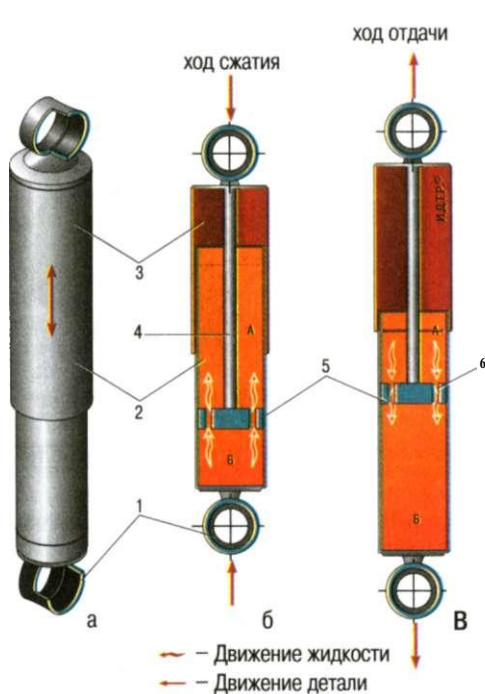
Схема работы амортизатора: а - внешний вид; б и в - принцип работы; 1 - проушина; 2 - рабочий цилиндр; 3 - кожух; 4 - шток; 5 - поршень; 6 - калиброванное отверстие; А и Б - полости цилиндра
